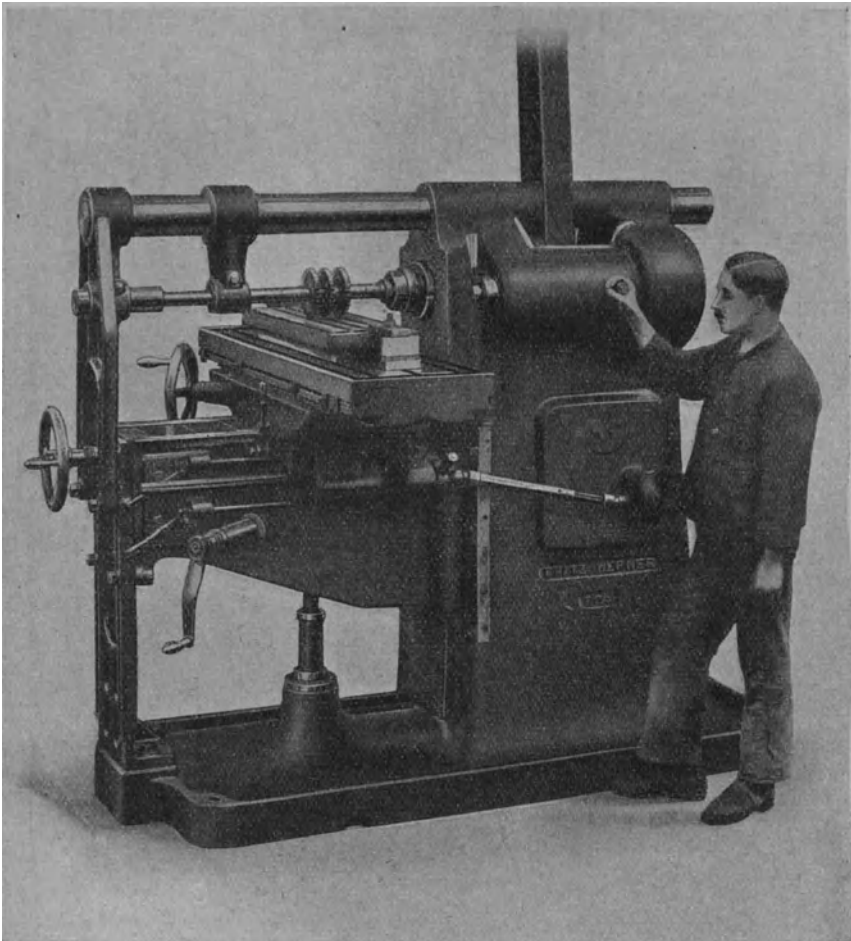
Wagerecht-Fräsmaschine von Friß Werner.
